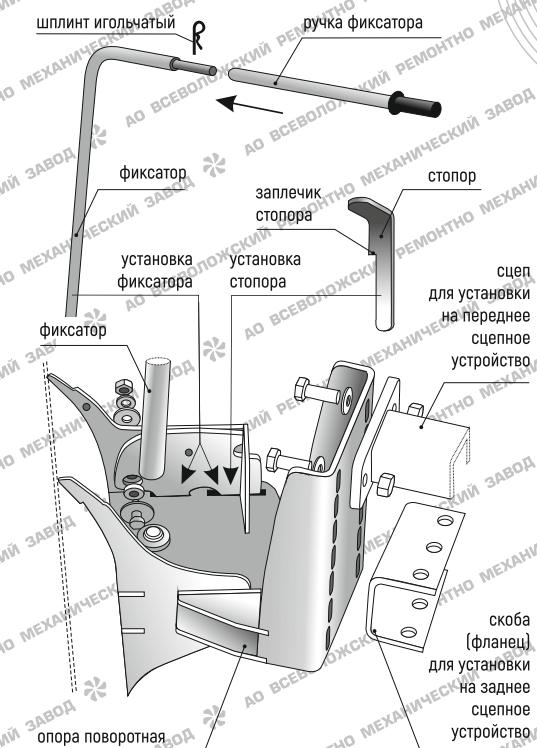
Сборка отвала, установка фиксатора (стопора)
